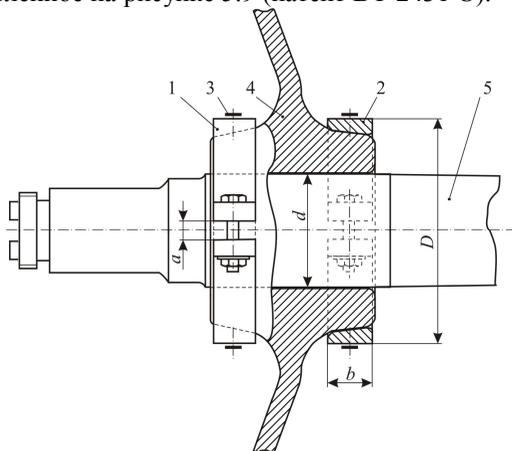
Устройство для контроля прочности механической запрессовки колеса на ось
